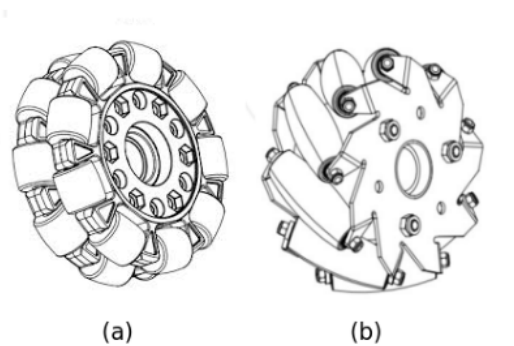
Rodas de desenho especial: (a) Universal, (b) Mecanum [6].
